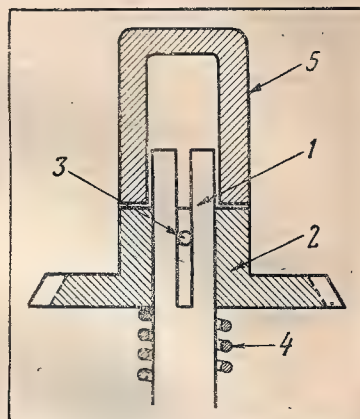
Механизм расцепления шестерен: 1 — вал, 2 — ведущая шестерня, 3 — шпилька, 4 — пружинка, 5 — нажимной колпак
